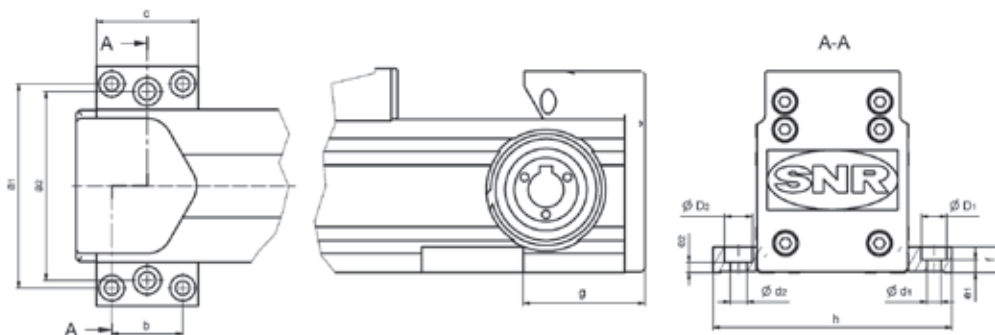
Abmessungen Befestigungsleisten AXC / AXDL
